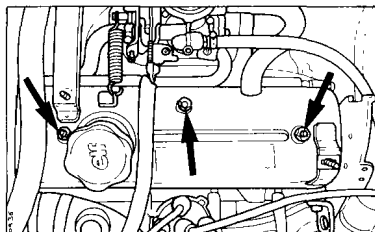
Гайки крепления крышки головки цилиндров (указаны стрелками)
